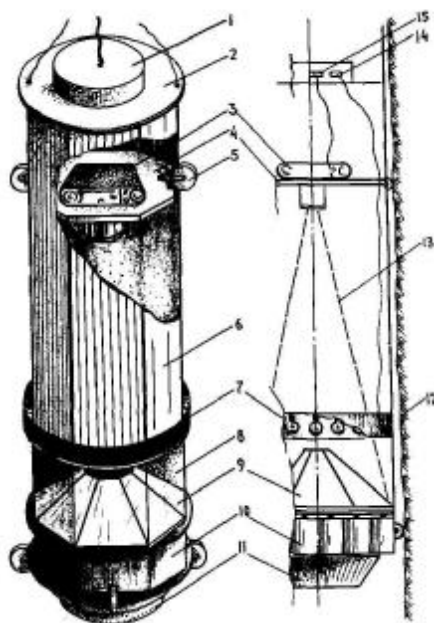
Конструкция скважинного информатоскопа: 1-крышка пульта управления; 2-верхняя крышка; 3-видеокамера; 4-полка для видеокамеры; 5-центрирующий ролик; 6-корпус прибора; 7-блок освещения; 8-стеклянный граненый цилиндр с мерной лентой; 9-зеркальная пирамида; 10-блокпитания; 11-направляющее устройство; 12-стенка скважины; 13-ход лучей объектива; 14-кнопки управления освещением; 15-кнопка управления съемкой
